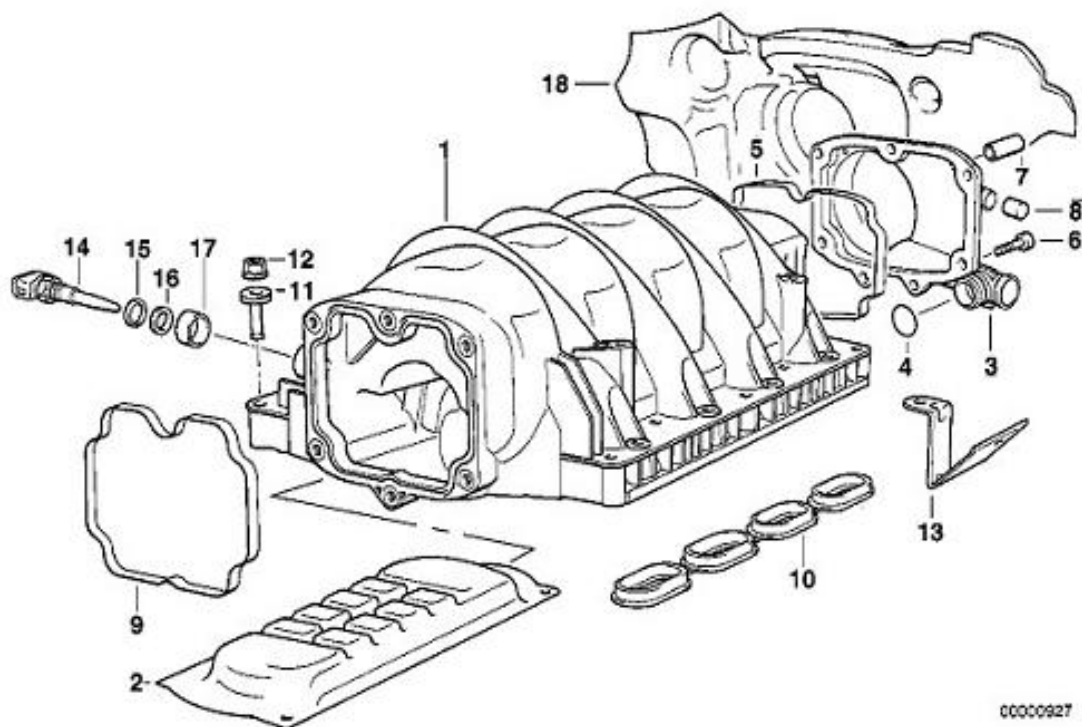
Конструкция впускного коллектора (ресивера) двигателя М60.
